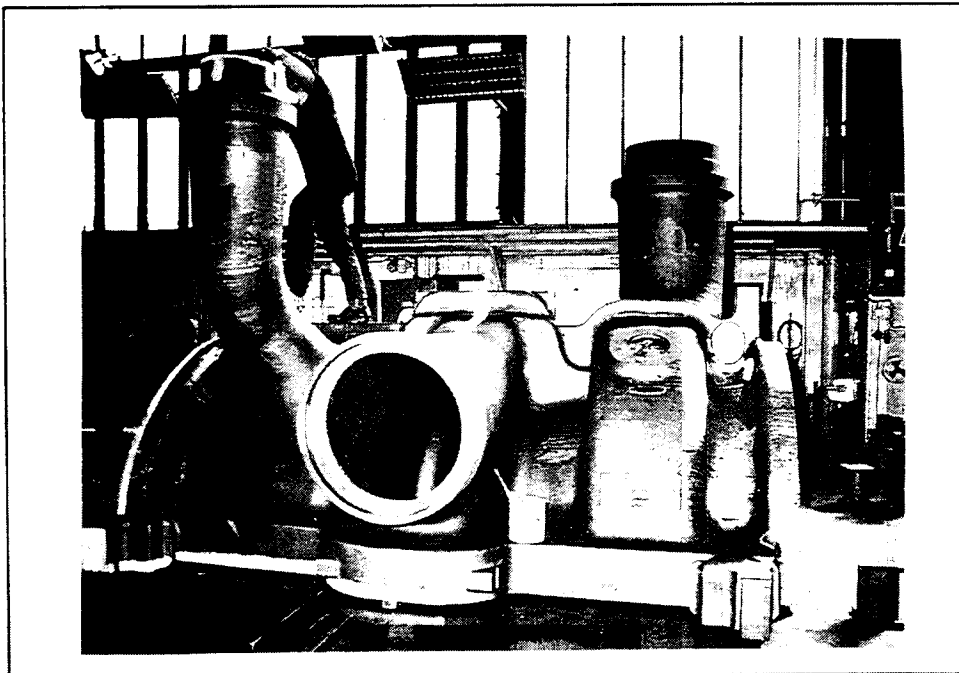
Mitteldruck - Innengehäuse mit angeschweißten Rohrstützen
